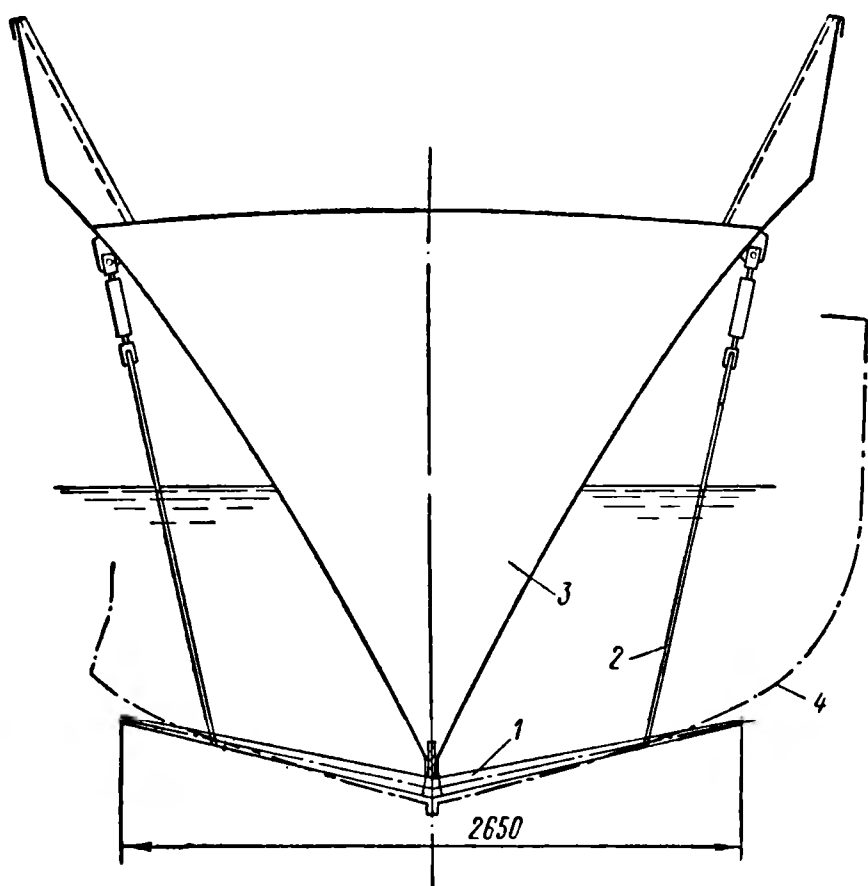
Установка успокоителя килевой качки на корпусе судна.
